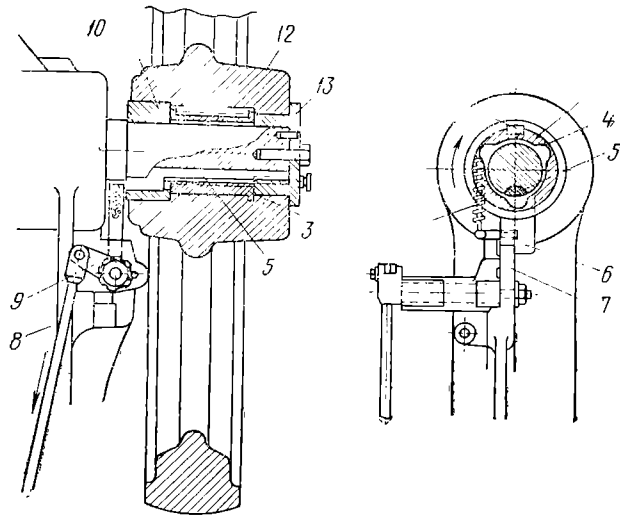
Жесткая муфта сцепления прессы одной поворотной шпонкой
